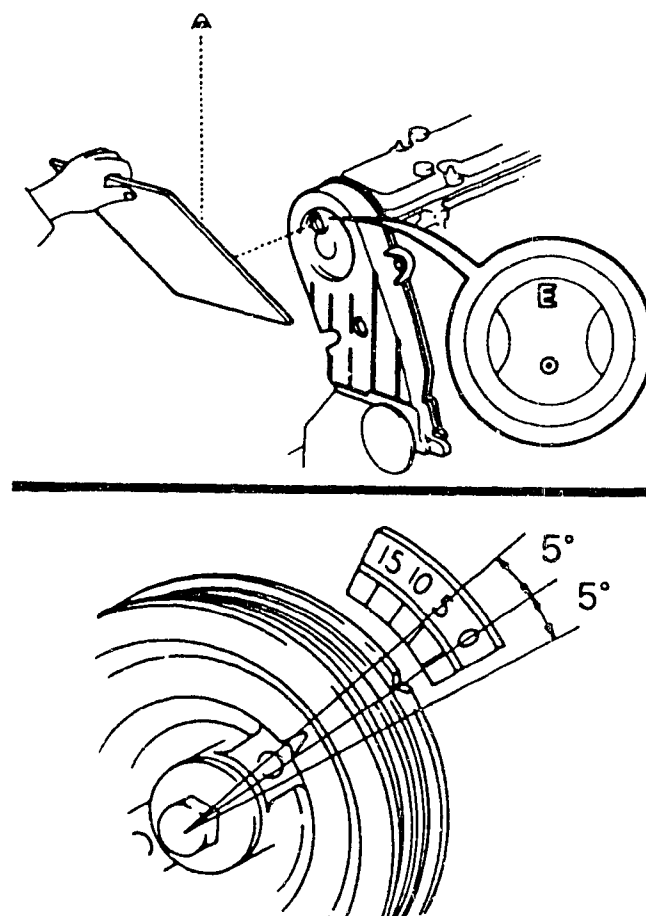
Motor 1S: Kontrolle der Steuerzeiten von aussen. oben) Die kleine Markierung am Gehäuse des Simmerings muss auf die Mitte der Bohrung im Nockenwellenrad ausgerichtet sein. – unten) Die Kurbelwelle muss $\pm 5^\circ$ vor oder nach OT stehen.
